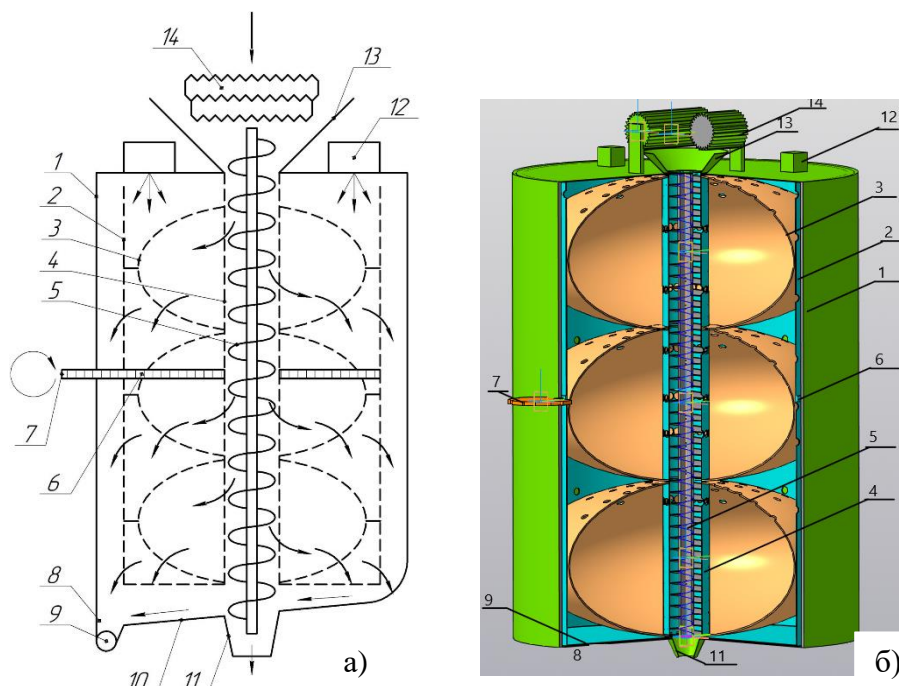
Размораживатель молозива животных непрерывно-поточного действия с СВЧ энергоподводом в коаксиальный резонатор: а – технологическая схема, б – общий вид, 1 – ферромагнитный цилиндрический экранирующий корпус; 2 – коаксиальный резонатор; 3 – перфорированные радиопрозрачные эллипсоиды; 4 – радиопрозрачный перфорированный цилиндр; 5 – ферромагнитный винтовой шнек; 6 – зубчатый венец; 7 – электроприводная шестерня; 8, 10 – ферромагнитная емкость приемная; 9 – приемная емкость для разогретого молозива; 11 – приемная емкость для отходов; 12 – магнетроны воздушного охлаждения; 13 – ферромагнитная емкость загрузочная; 14 – измельчающий механизм
